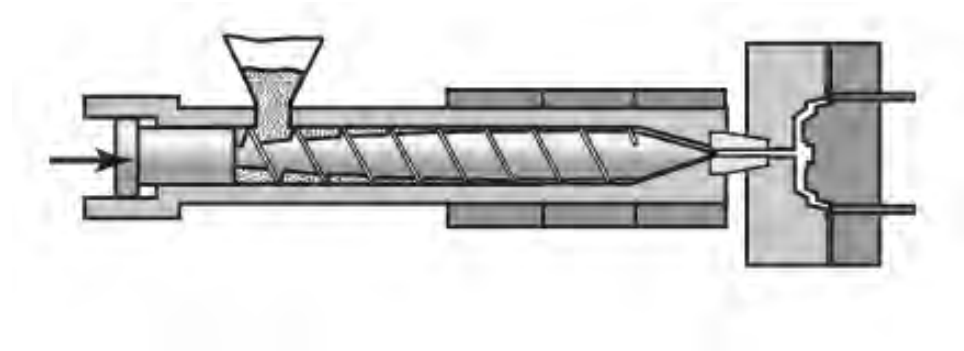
Ilustración de una máquina de moldeo por inyección que funciona con un tornillo giratorio para forzar el material en el molde de la pieza a fabricar. Tomado de [67].
